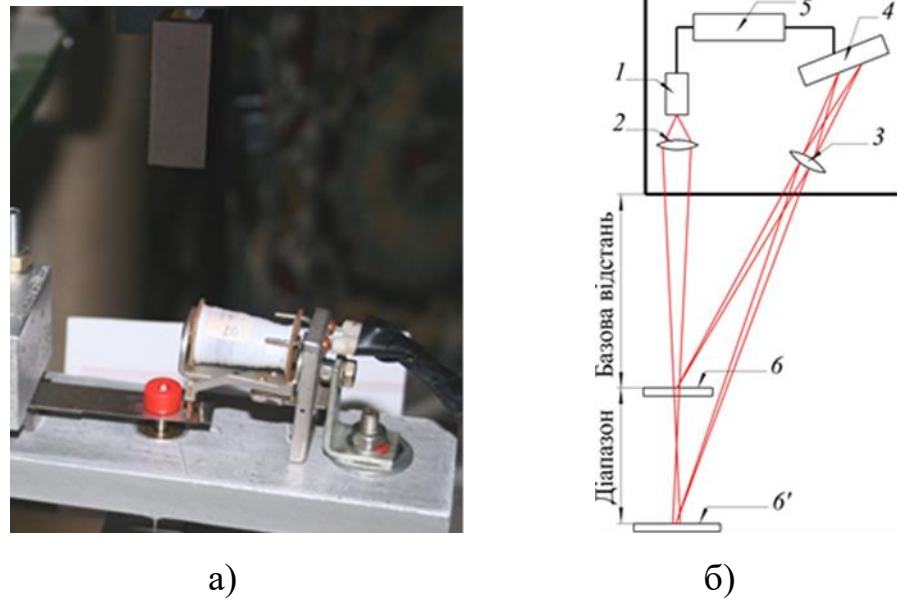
Установка для визначення профілю бокової поверхні різь: а) пристрій для фіксації координат; б) схема лазерного триангуляційного вимірювача RIFTEK
